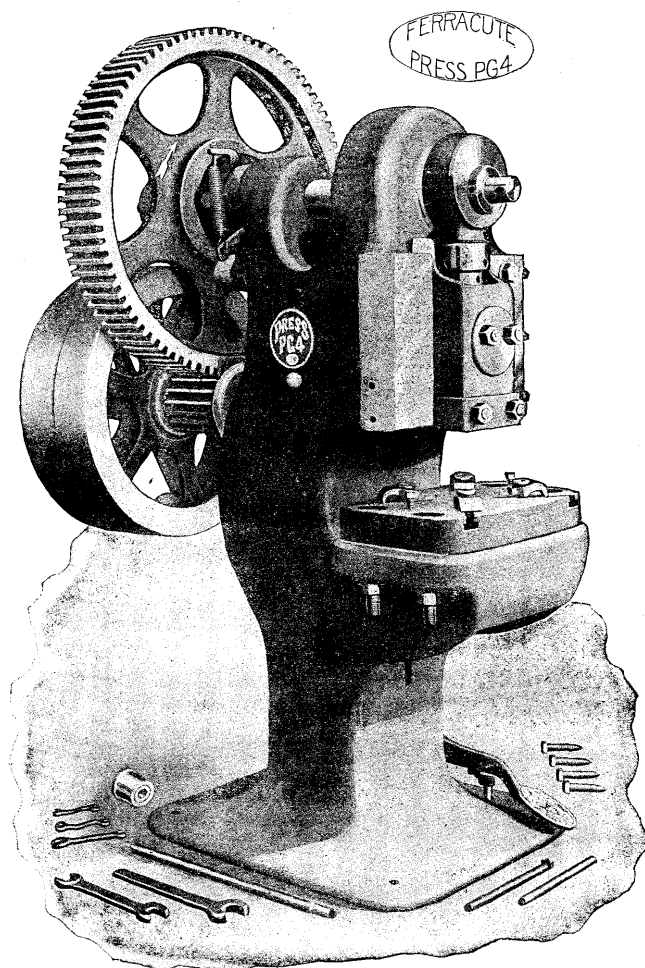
Presse à poinçonner à engrenage, de la Ferracute Machine Company, de Bridgeton (E.U.).
